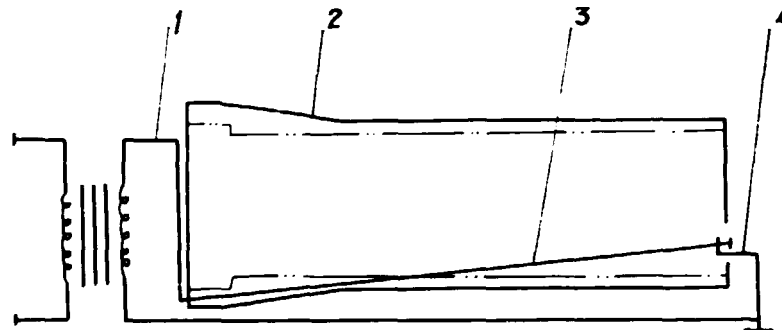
Conexión del soldador por arco y el segmento de acero
